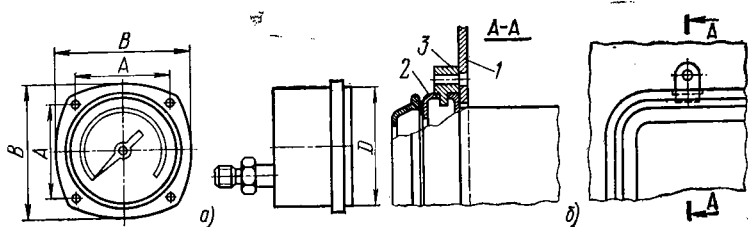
Крепление приборов с лицевой стороны щита.
